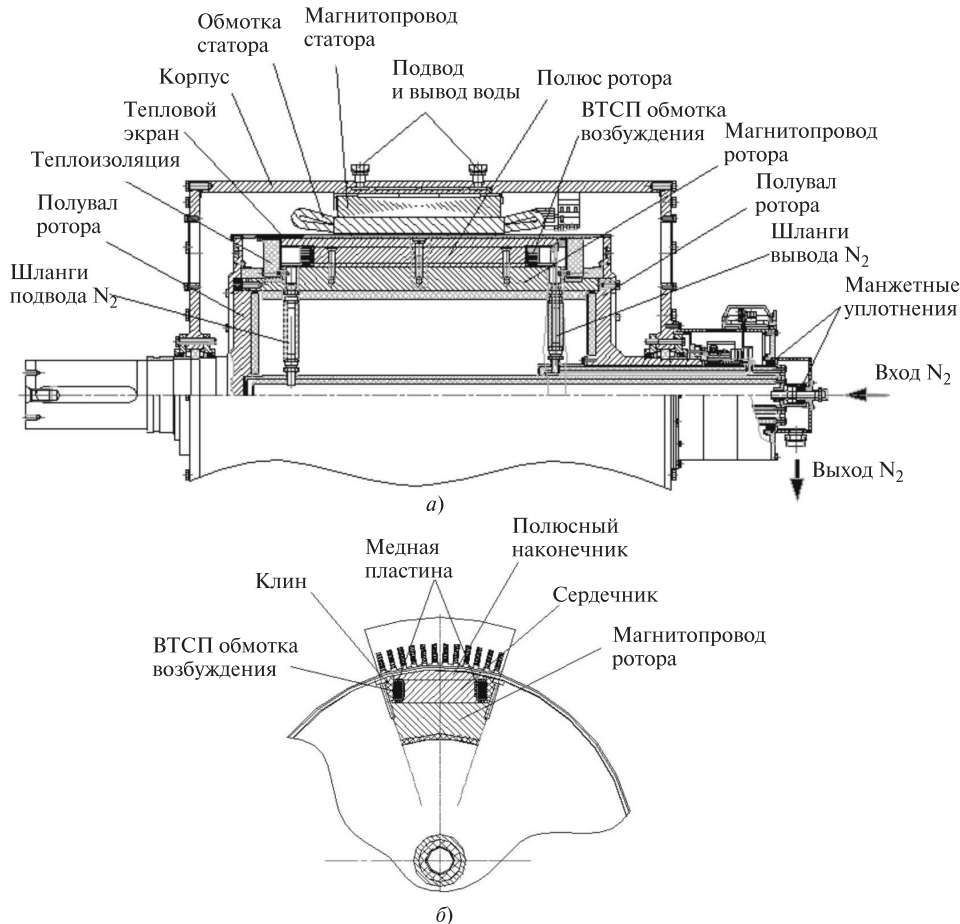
Общий вид опытного образца СПСГ мощностью 1 МВА с щеточной системой подачи тока в обмотку возбуждения: а — продольный разрез; б — поперечный разрез
